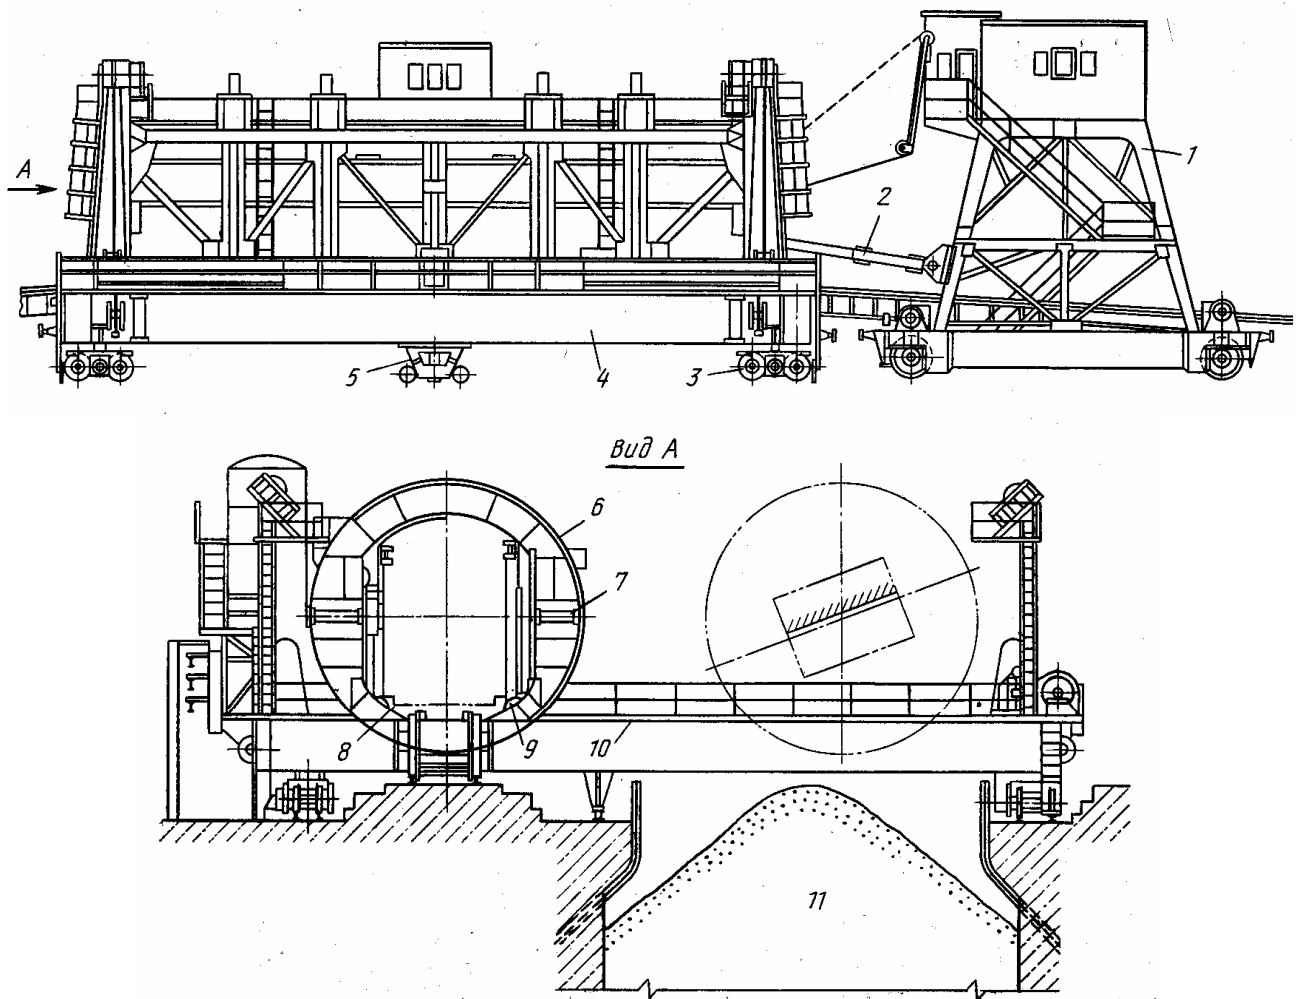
Передвижной круговой вагоноопрокидыватель
